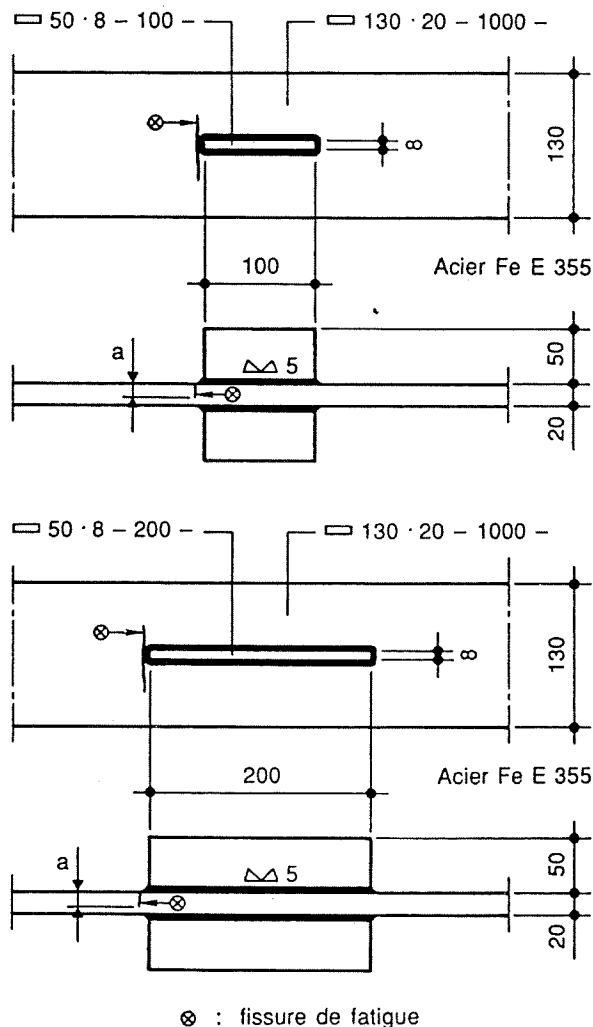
Géométrie des éprouvettes utilisées (dimensions en mm, longueur totale des éprouvettes : 1'000 mm), tiré de [1]
